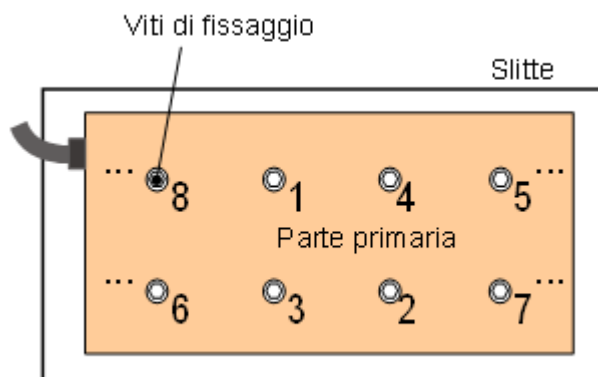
Sequenza di serraggio viti di fissaggio parte primaria
